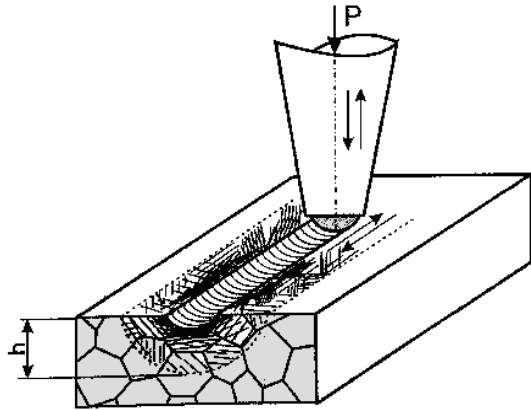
Схема поверхностной ультразвуковой обработки с формированием единичной дорожки
